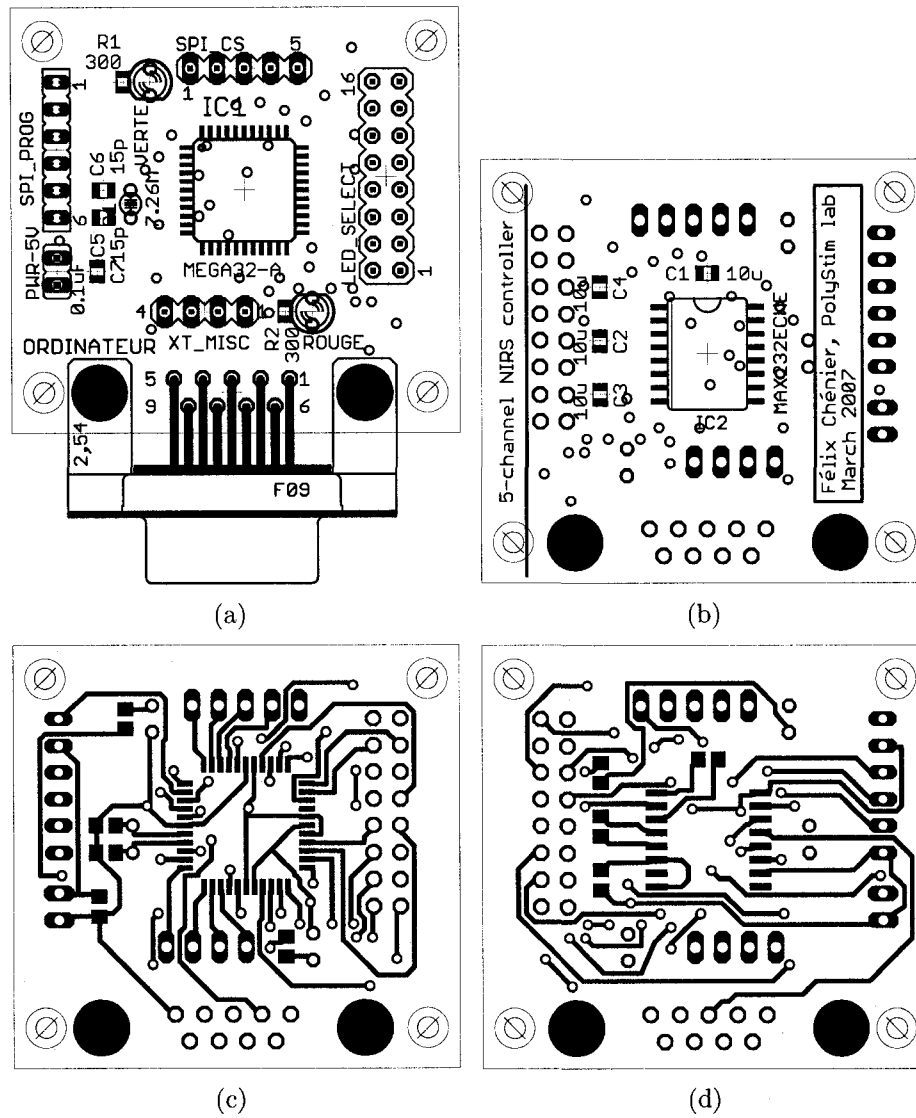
Circuit imprimé du contrôleur. (a) Composantes, dessus. (b) Composantes, dessous. (c) Traces, dessus. (d) Traces, dessous.
